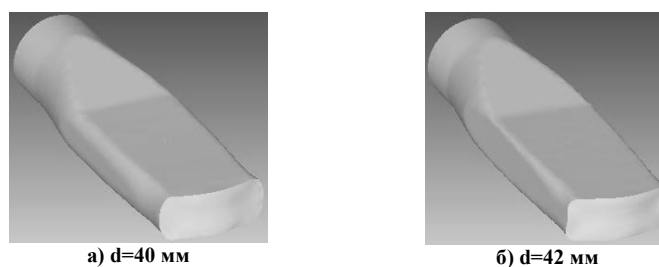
Здеформовані заготовки, які отримані в матриці з деформуючою поверхнею у вигляді призми
